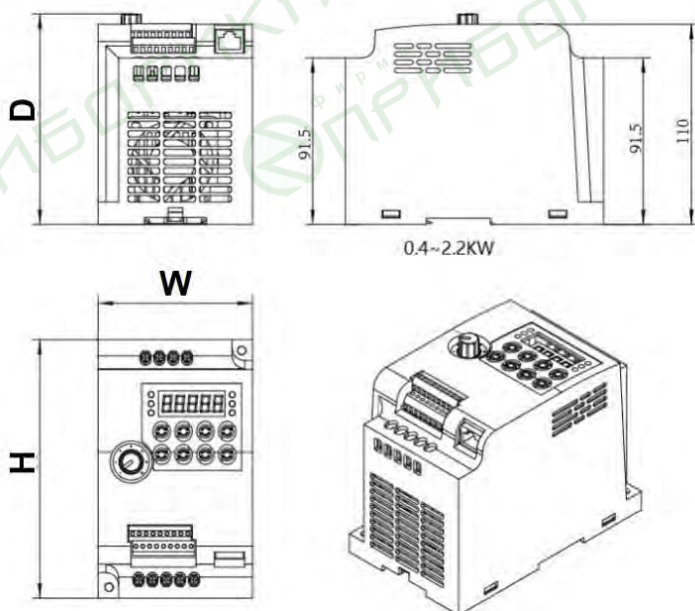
Внешний вид, габаритные и монтажные размеры Преобразователя 200MN[03] в пластиковом корпусе
